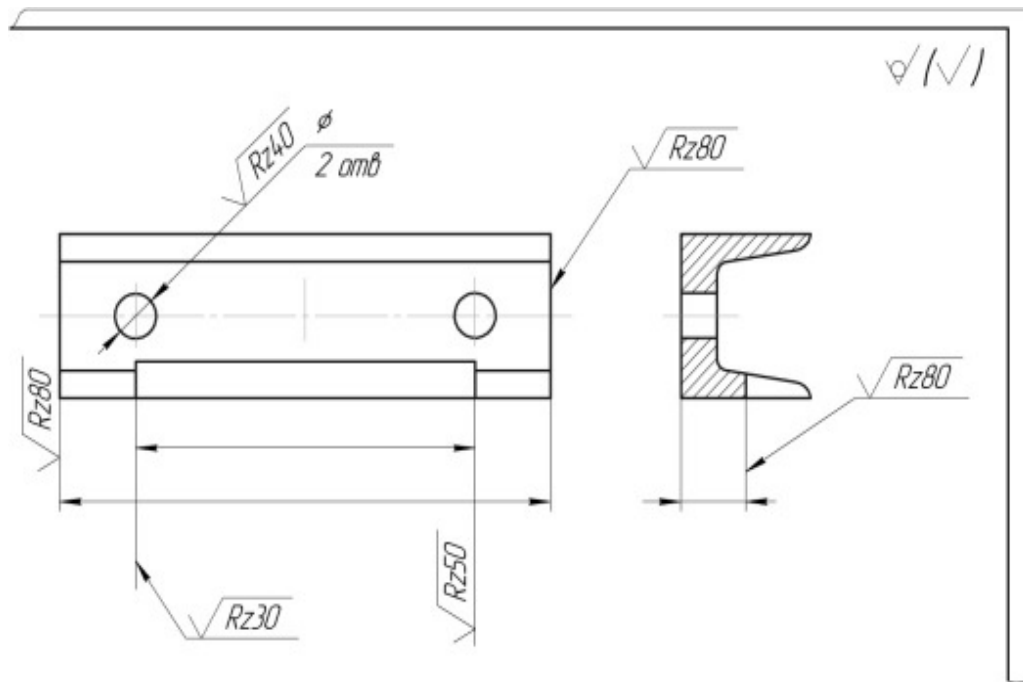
Указание шероховатости, когда большая часть поверхностей не обрабатывается по данному чертежу
